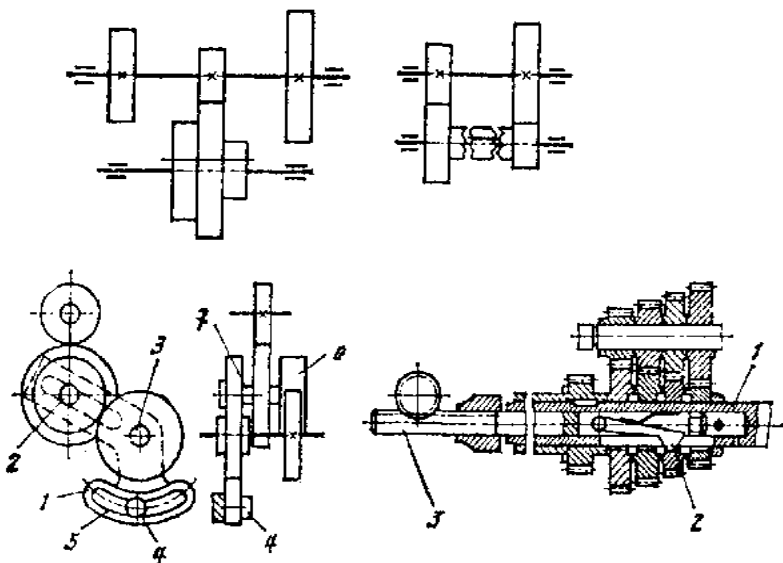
Зубчаті механізми металорізальних верстатів:
